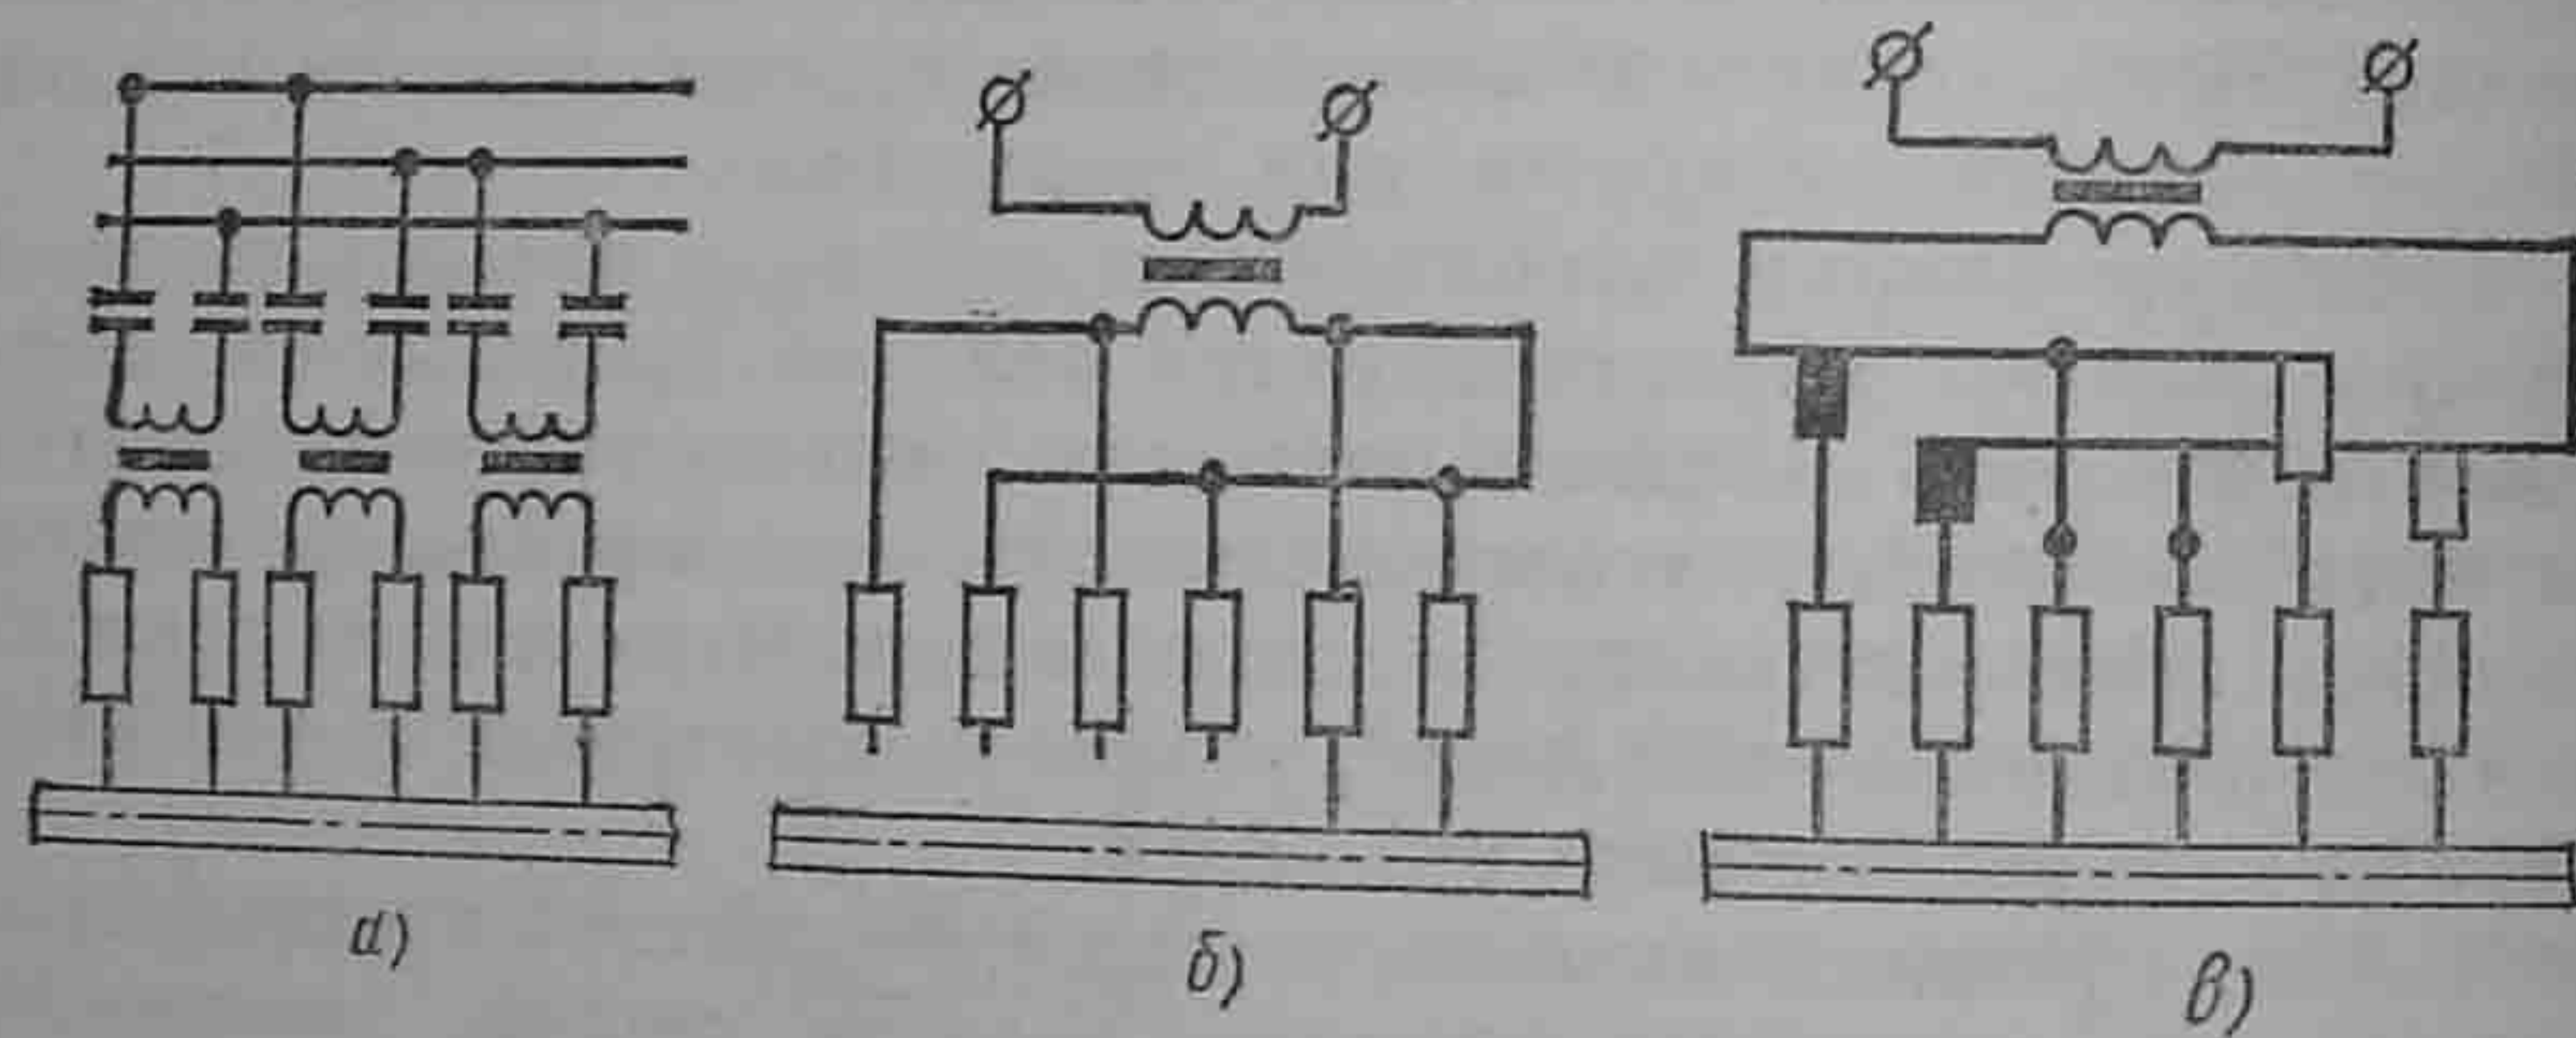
Схемы многосторонней точечной сварки
